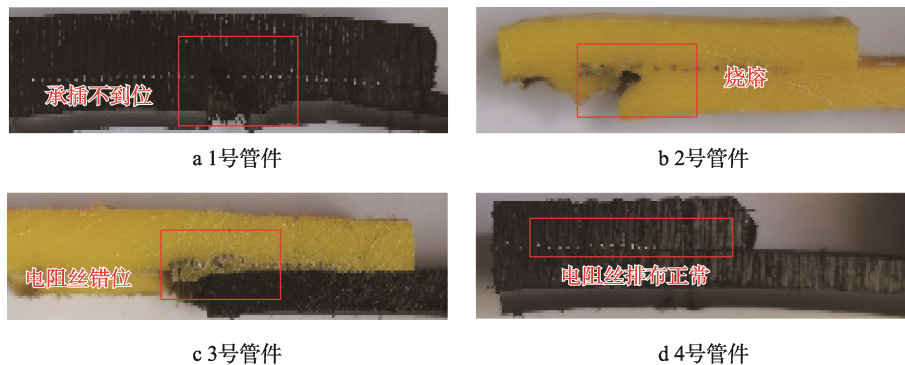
管件电熔焊接截面典型部位宏观照片
